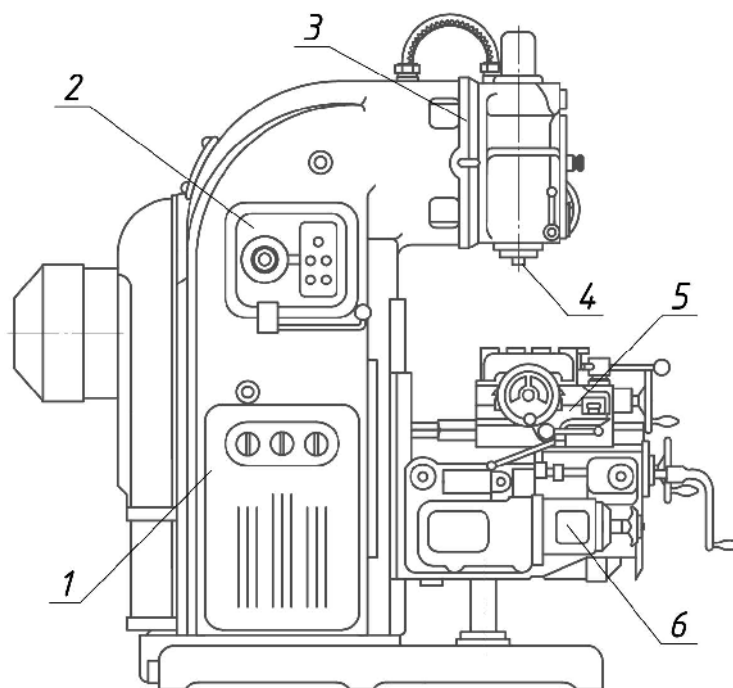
Загальний вигляд вертикально-фрезерного верстату
